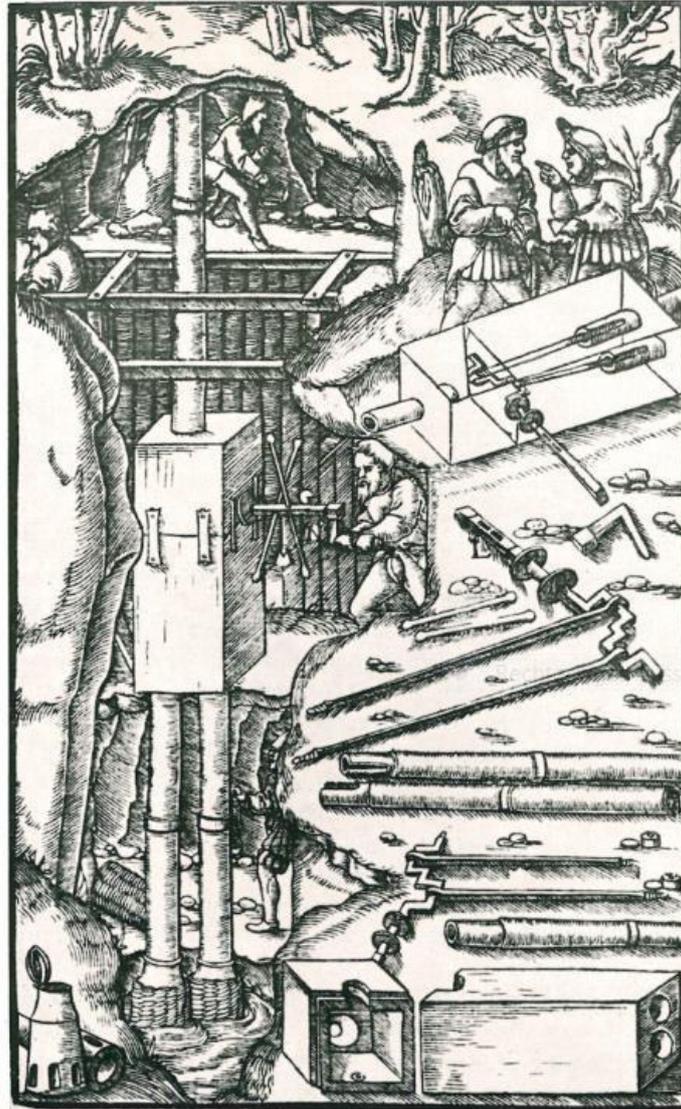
Maschinenzeichnung. Holzschnitt aus Georg Agricola, *De Re Metallica*, 1556.
